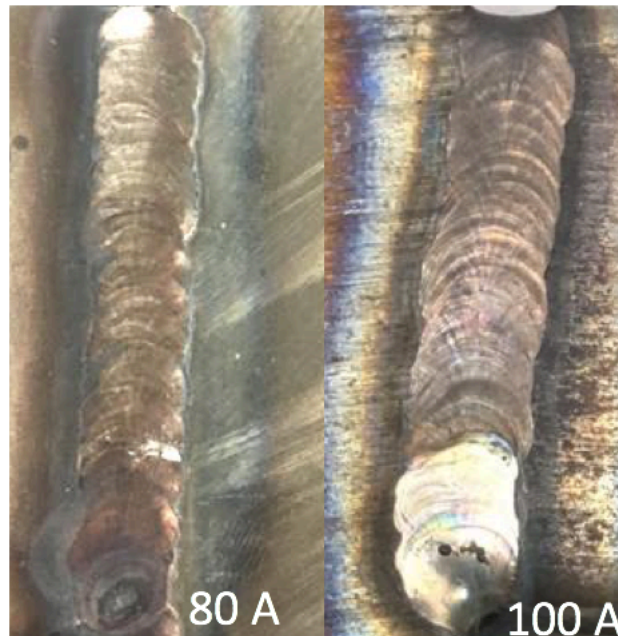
Cordones de soldadura de las probetas de ensayo de tensión.
